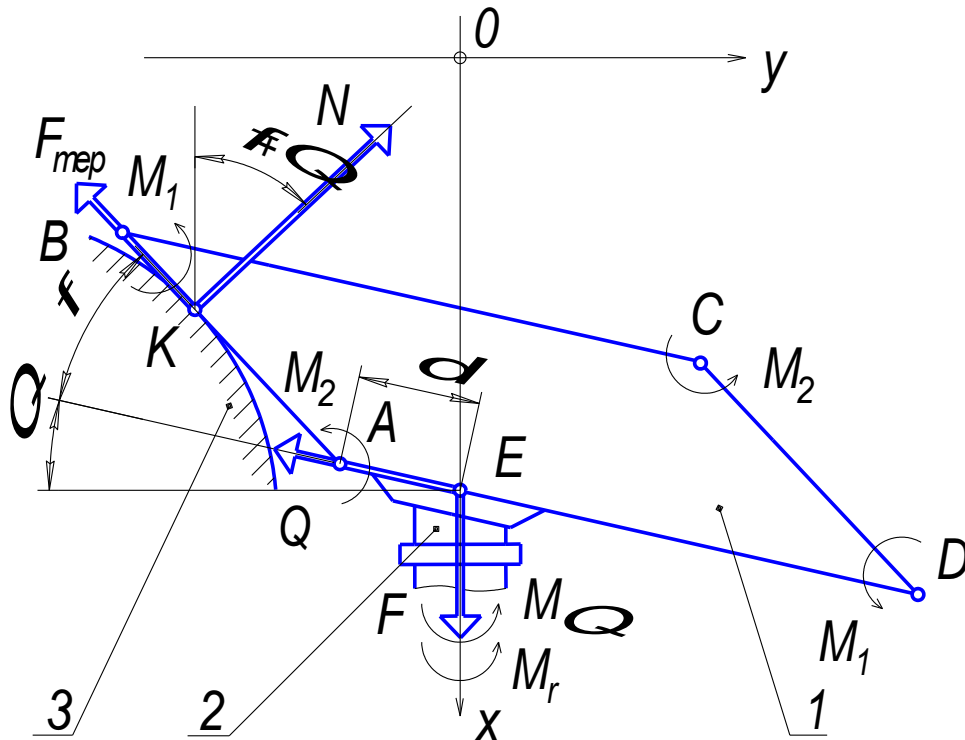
Розрахункова схема силової взаємодії заготовки з копіром
